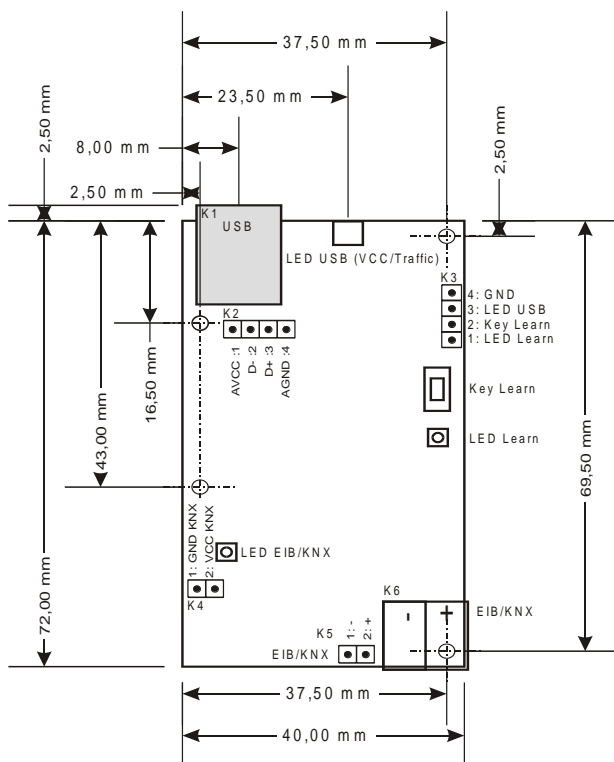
Lageplan Bohrungen, Belegung Anschlüsse
